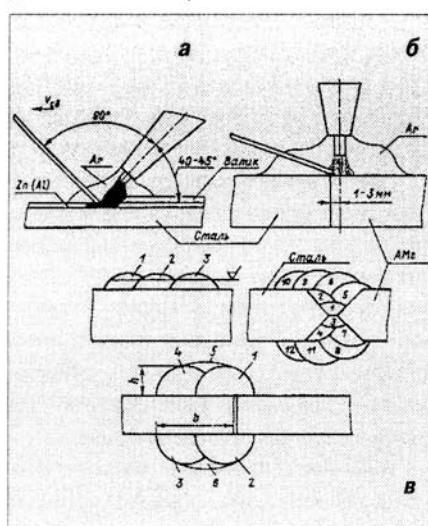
Аргонодуговая сварка и наплавка алюминия по стали:
